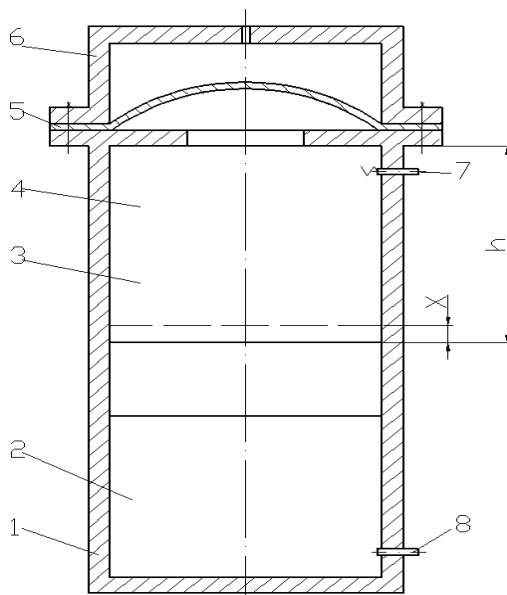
Расчетная схема рабочего процесса двухкамерного устройства для газовой штамповки: 1 – корпус; 2, 4 – камеры сгорания; 3 – поршень; 5 – штампующая заготовка; 6 – матрица; 7, 8 – свечи зажигания
